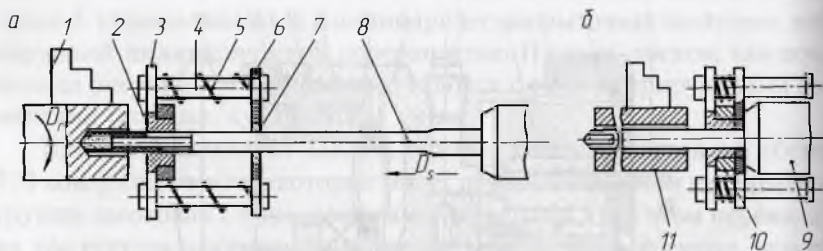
Устройство для направления и повышения жесткости прямых сверл для глубокого сверления:
